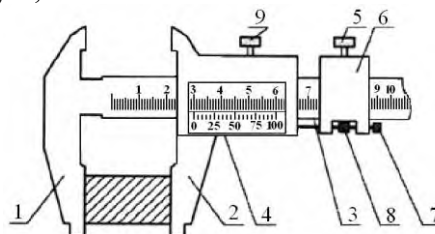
Штангенциркуль ШЦ-ІІ
